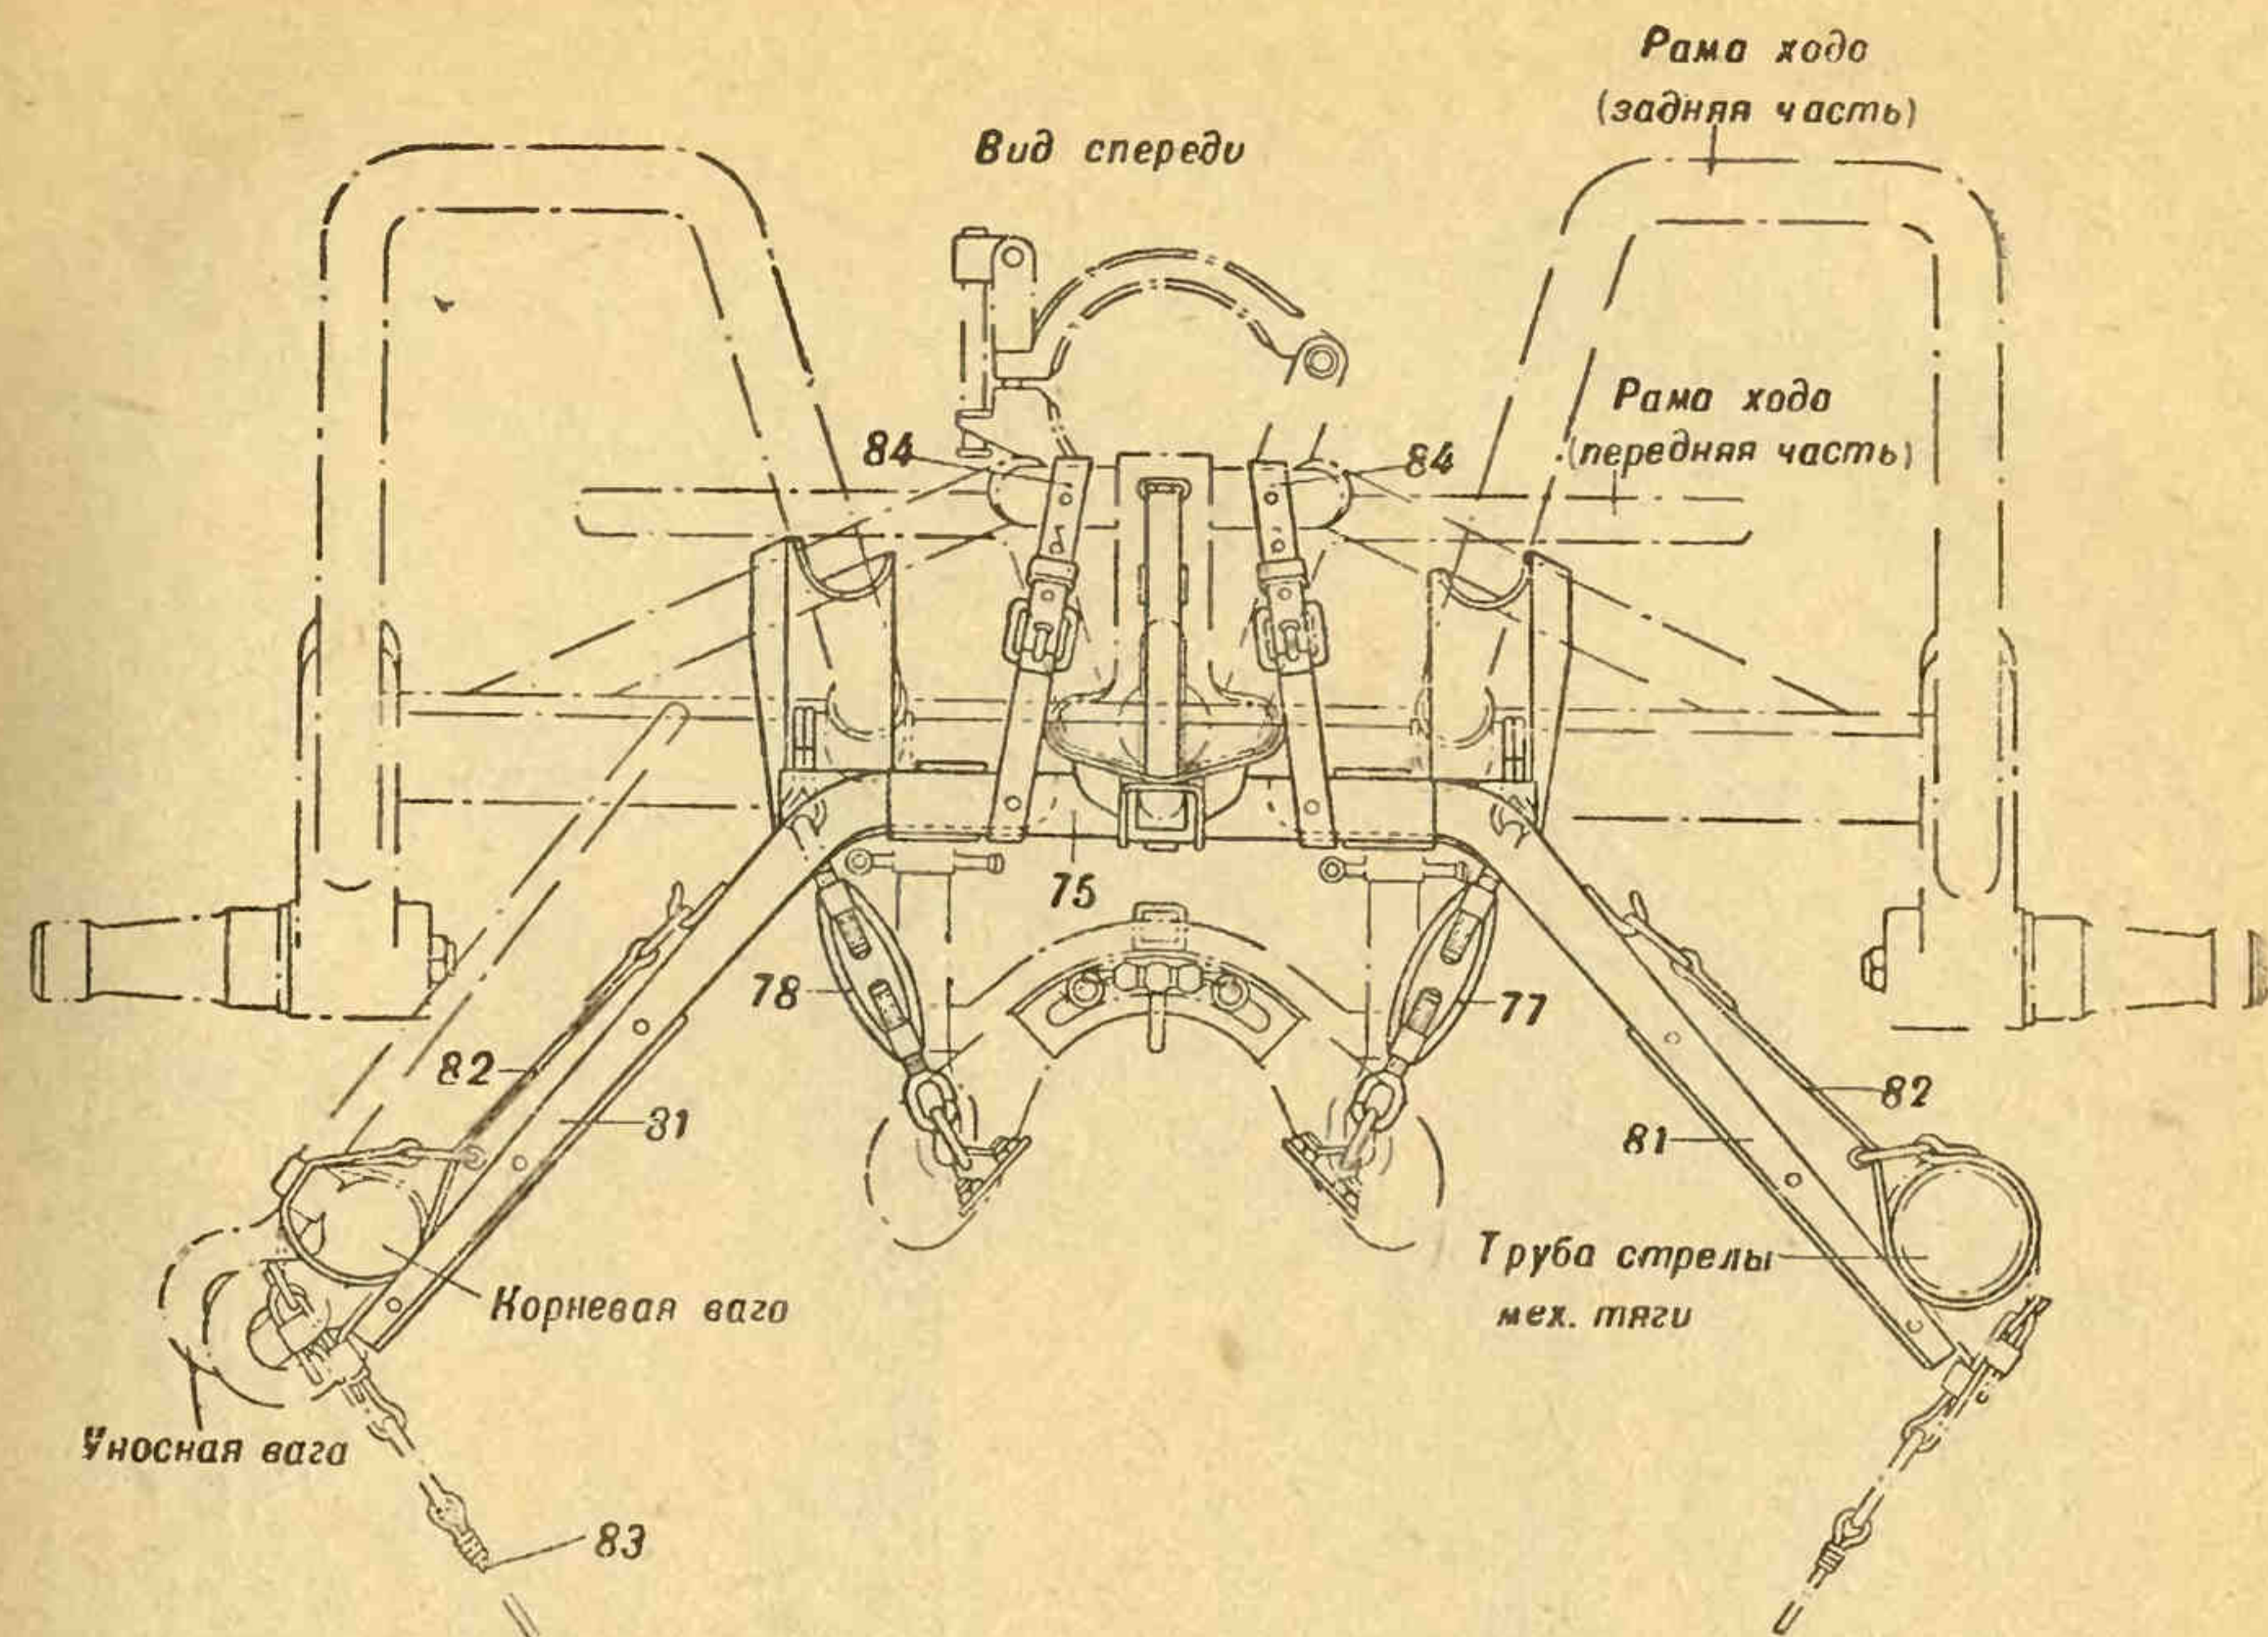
Укладочное приспособление № 5 (вид слева и спереди):
